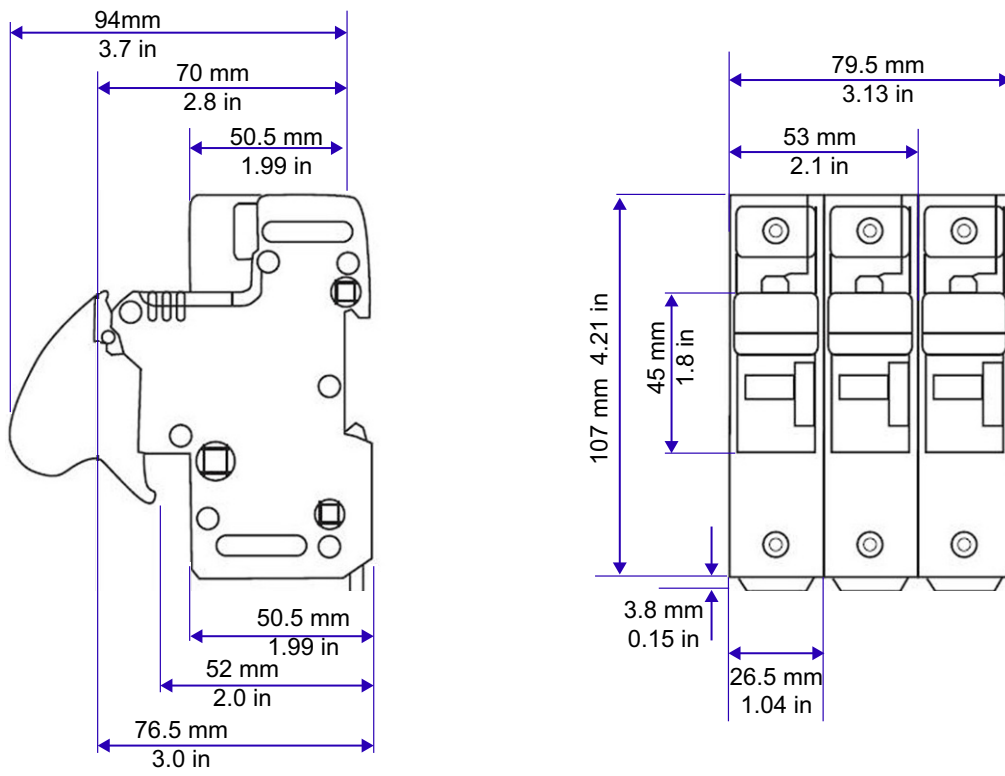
Dimensions des porte-fusibles : US143 (14x51 mm)
